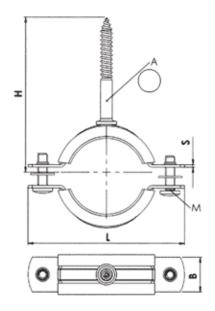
Хомут для крепления воздуховодов высокой нагрузки
